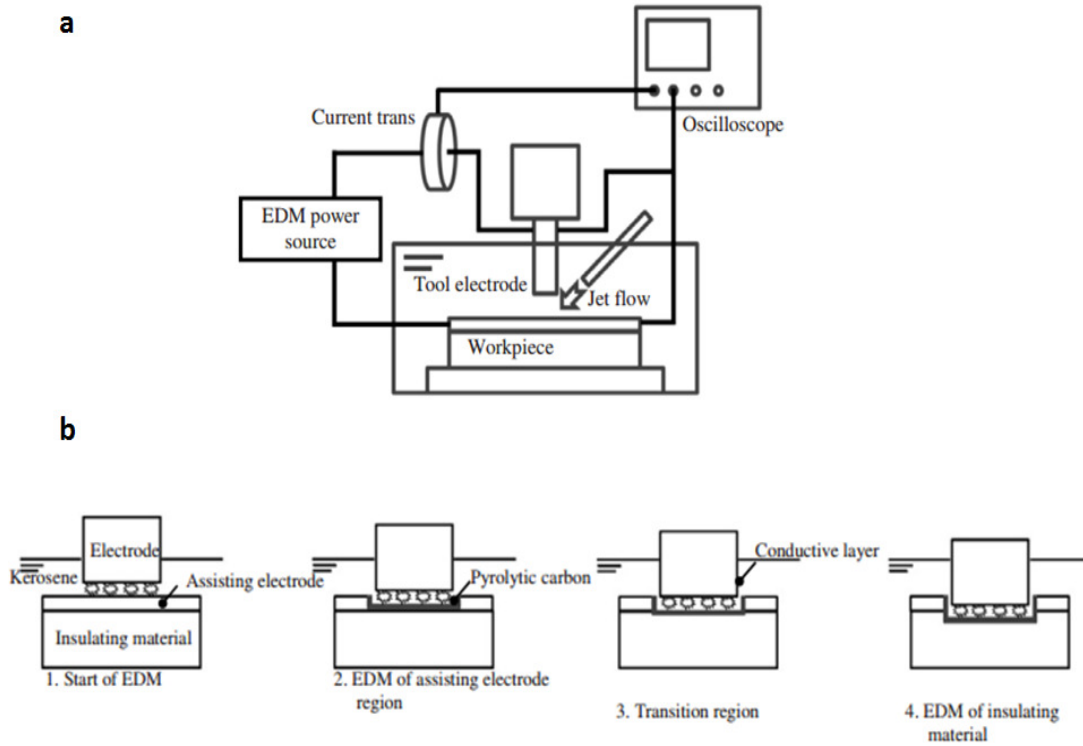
a) Montaje experimental de la técnica de EDM donde la herramienta-electrodo, consiste en una punta cilíndrica de cobre. b) Proceso de EDM asistido por electrodo [9].
